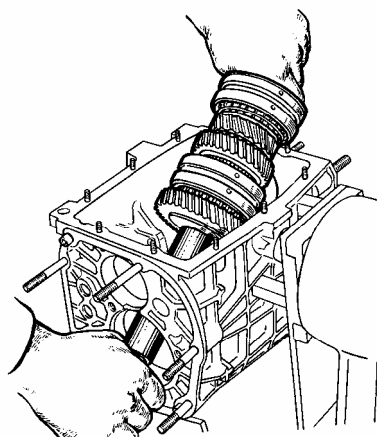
Извлечение вторичного вала из картера коробки передач
